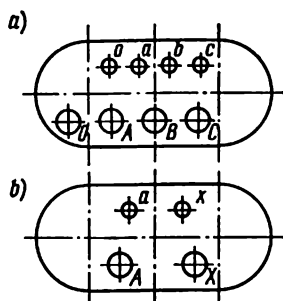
Repérage des bornes sur le couvercle d'un transformateur à deux enroulements:
